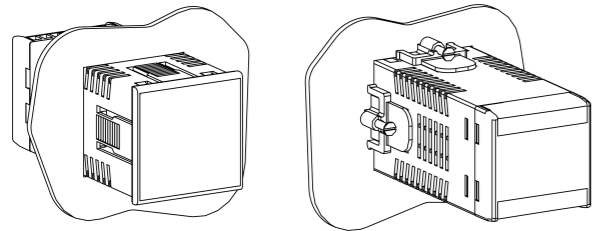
Монтаж прибора щитового крепления Щ5
